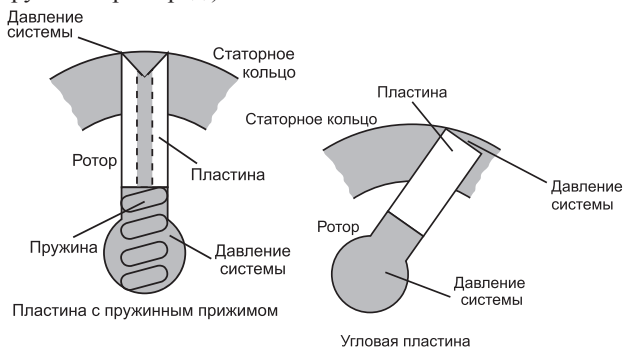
Пластина с пружинным прижимом (слева) и угловая пластина
